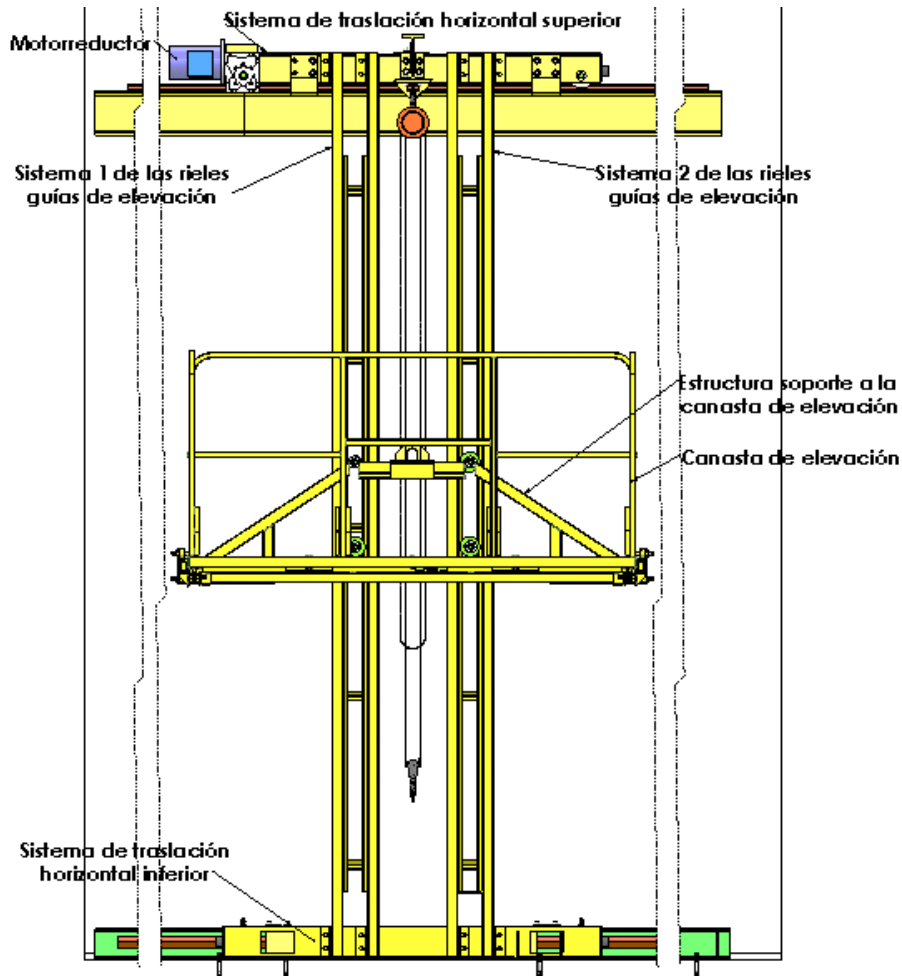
Sistemas 1 -2 de las rieles guías de elevación
